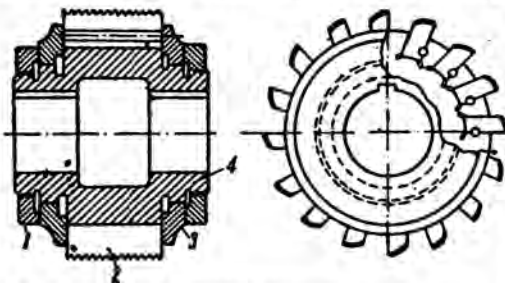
Резьбовая цилиндрическая фреза со вставными зубьями.
